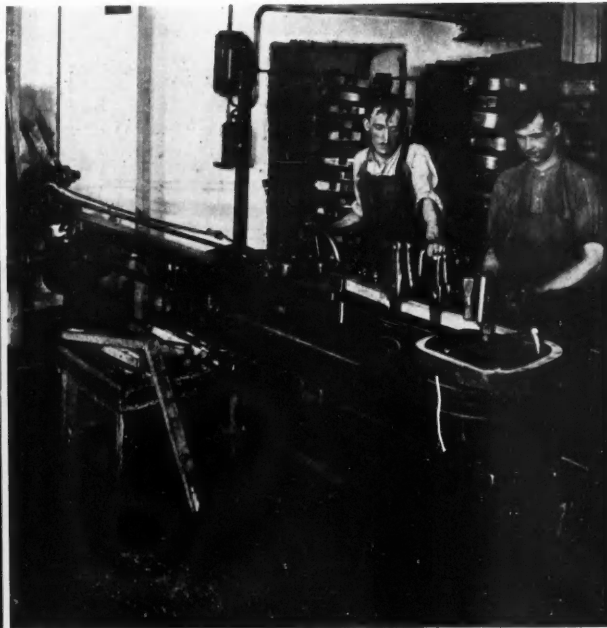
MACHINE A COURBER LES CHASSIS DE SIÈGE. LE BOIS VIENT S'ENROULER AUTOUR D'UNE FORME MOBILE QUI L'ACCOMPAGNE AU SÈCHAGE.
